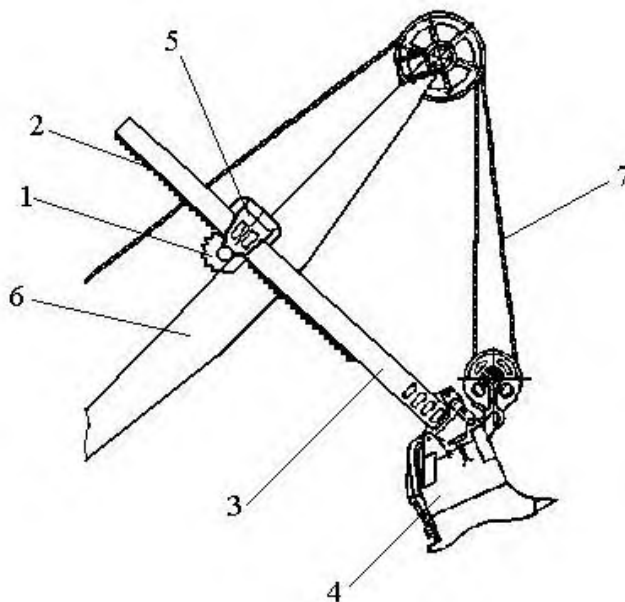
Зубчато-реечный механизм напора: 1 – кремальберная шестерня; 2 – зубчатая рейка; 3 – рукоять; 4 – ковш; 5 – седловой подшипник; 6 – стрела; 7 – подъемный канат
